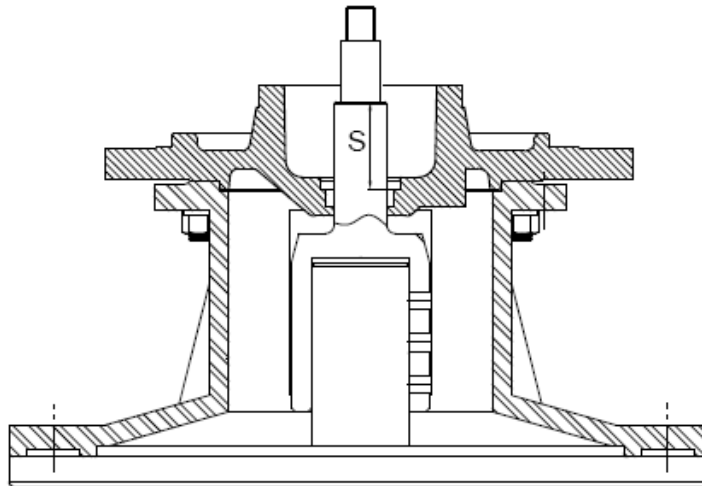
Ensamblaje del eje de la bomba en el eje del motor eléctrico
